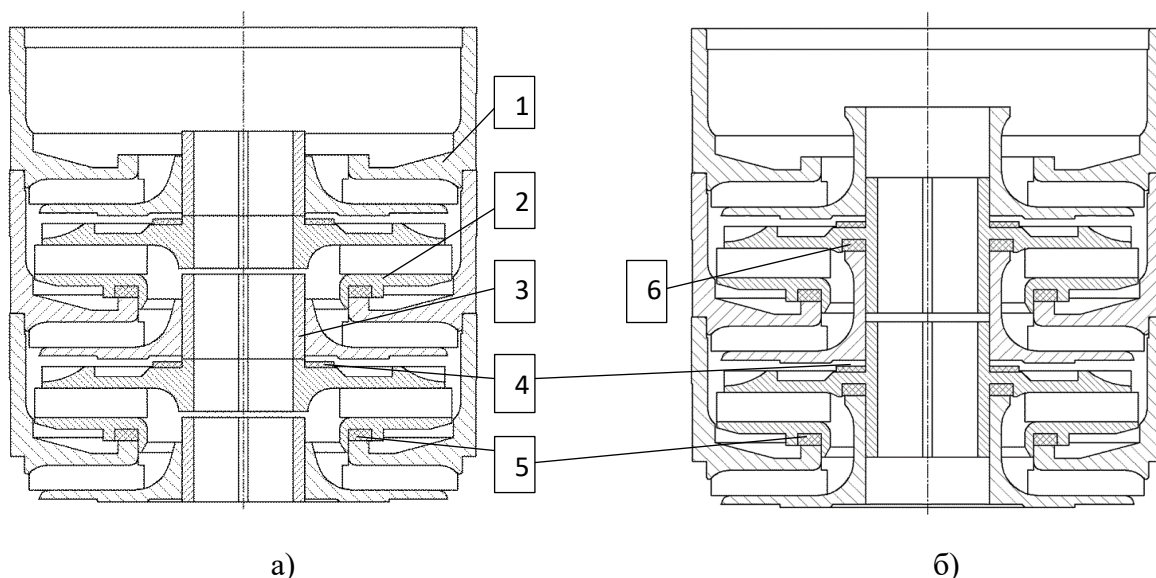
Конструкция ступени нефтяной: а) – одноопорная конструкция; б) – двухопорная конструкция; 1-направляющий аппарат, 2-рабочее колесо, 3-втулка вала, 4-шайба верхняя, 5-шайба нижняя большая, 6- шайба нижняя малая
